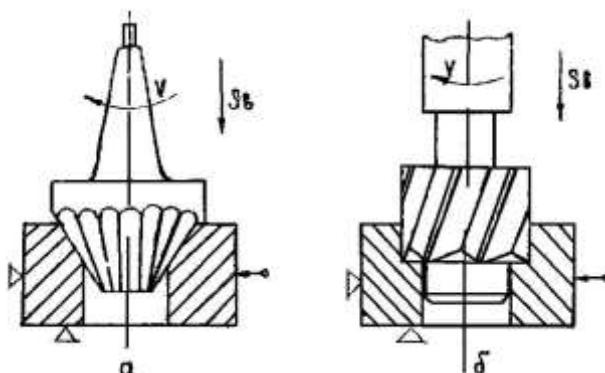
Схеми різання конічним /а/ та циліндричним /б/ зенкером.
